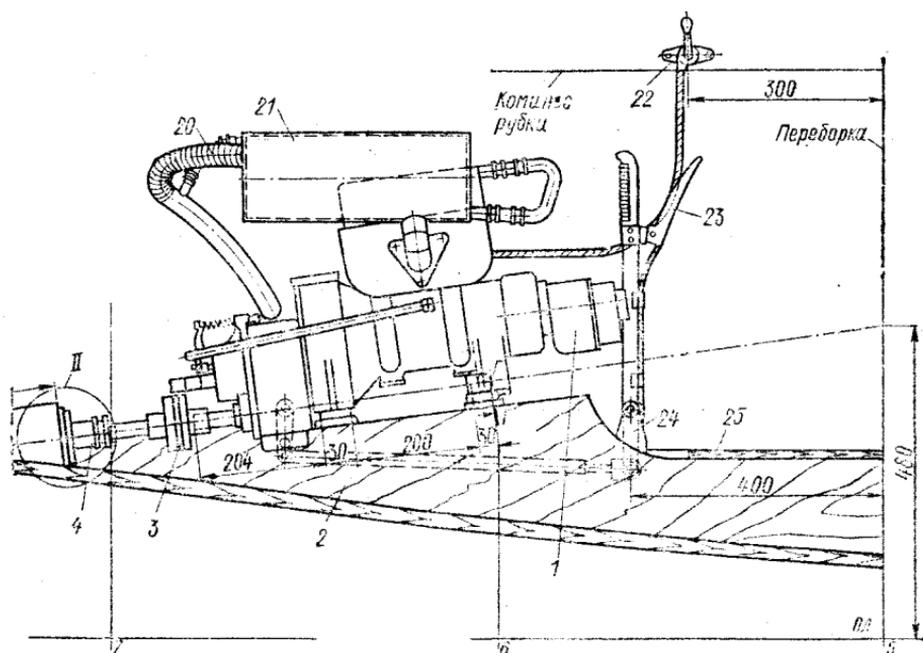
, а. Монтажный чертеж механической установки с двигателем «СМ-557Л». Поперечное сечение — см. на стр. 206.
